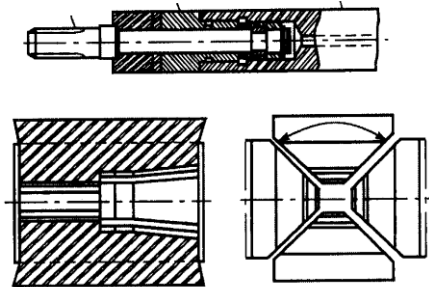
Загальний вигляд складної оправки і робочих кулачків для редукування внутрішньої поверхні корпусу муфти:
